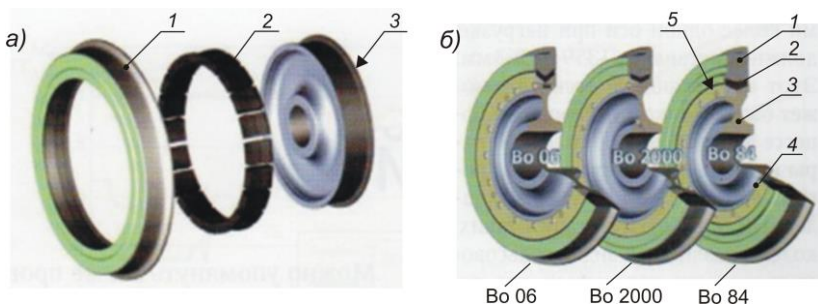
Конструкции колес с одним резиновым кольцом:
